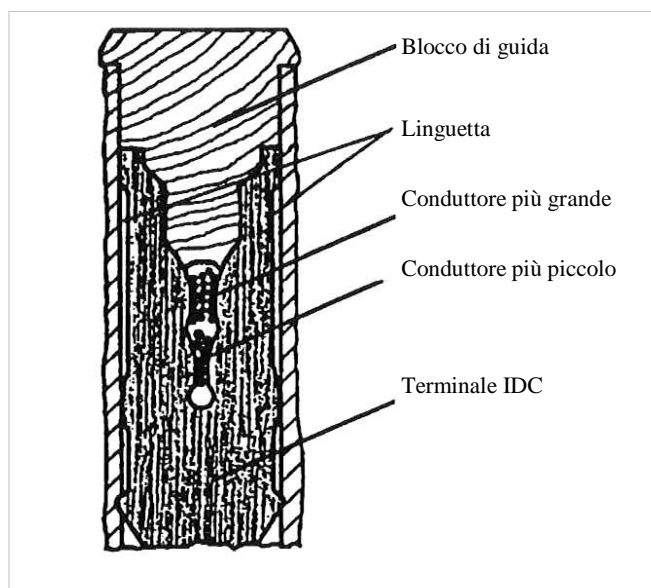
Connessione IDC non accessibile con due conduttori di diversa sezione in una fessura di connessione.
